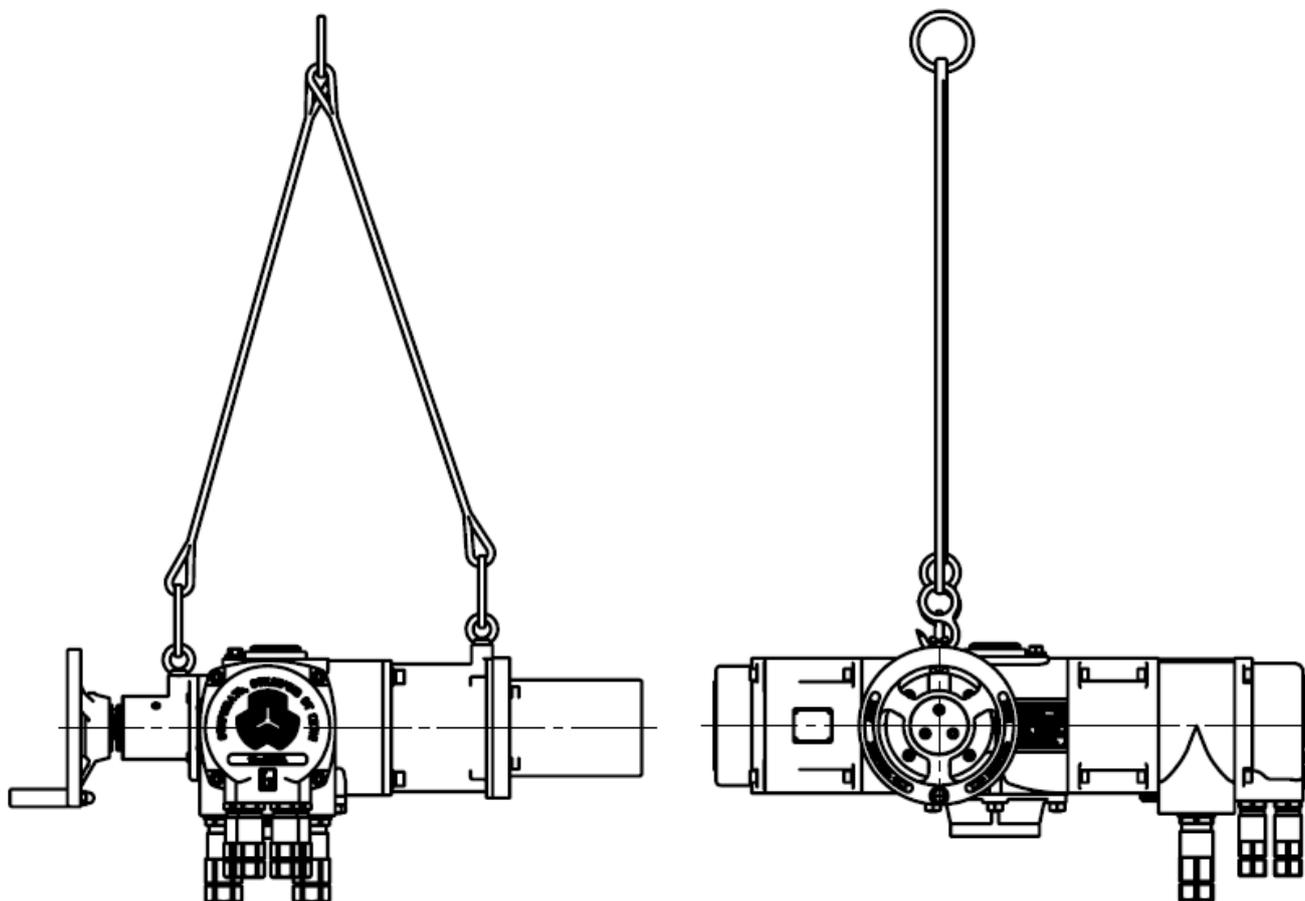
б – Схема строповки привода конструктивной схемы 41
